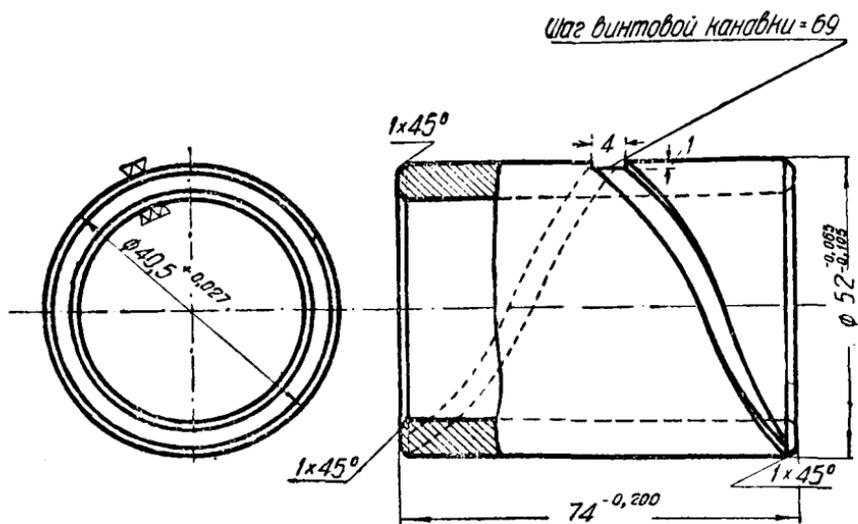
Дет. № 78. Втулка цилиндрической шестерни верхнего вала коробки передач
